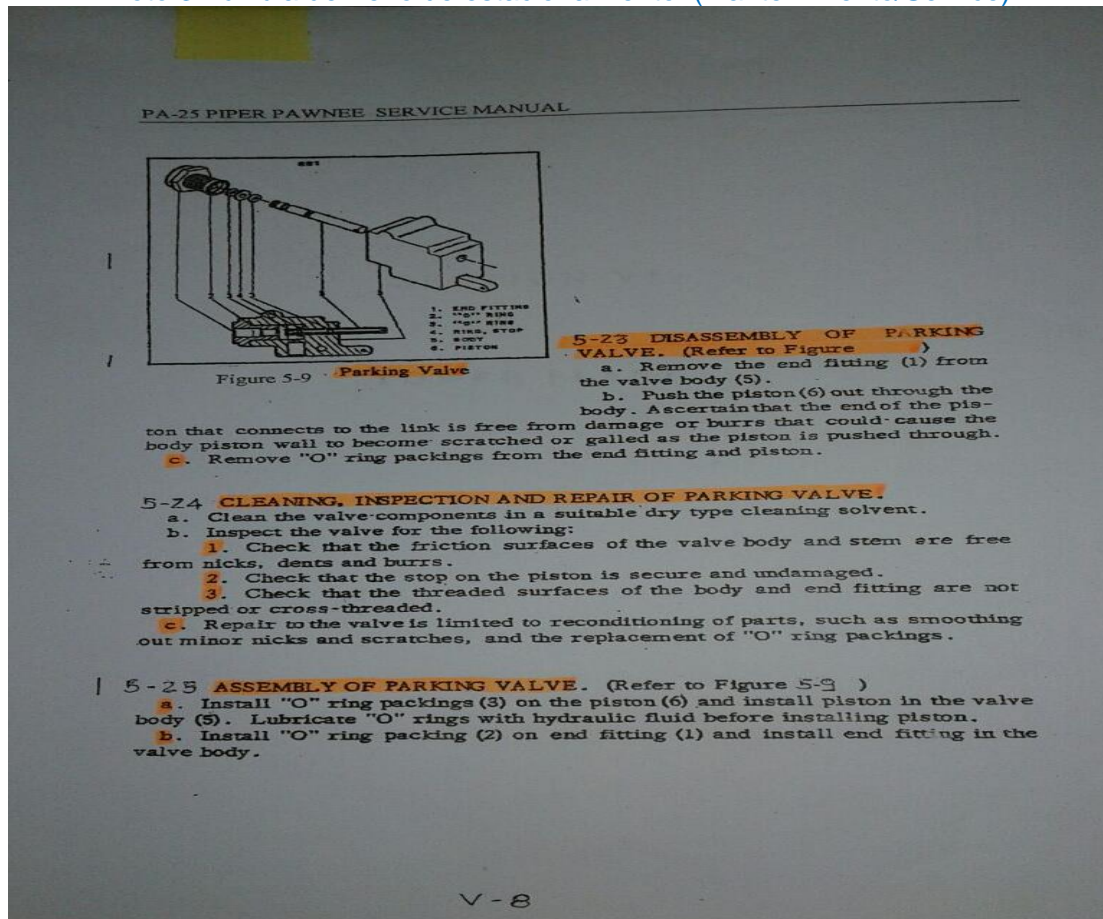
Detalles de la válvula Parking Brake (freno de estacionamiento).
